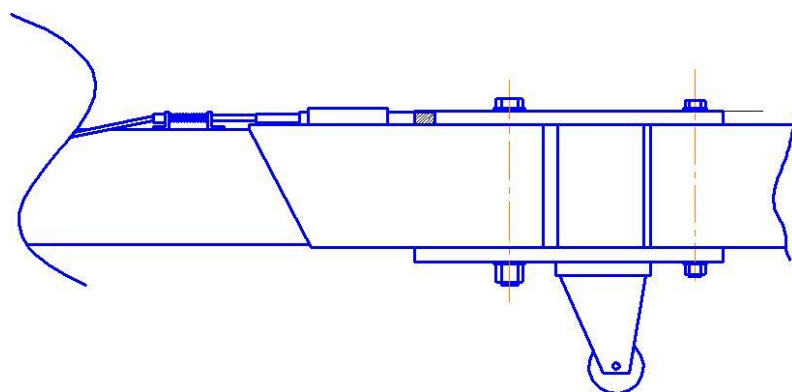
Поворотный механизм (вид сбоку)
